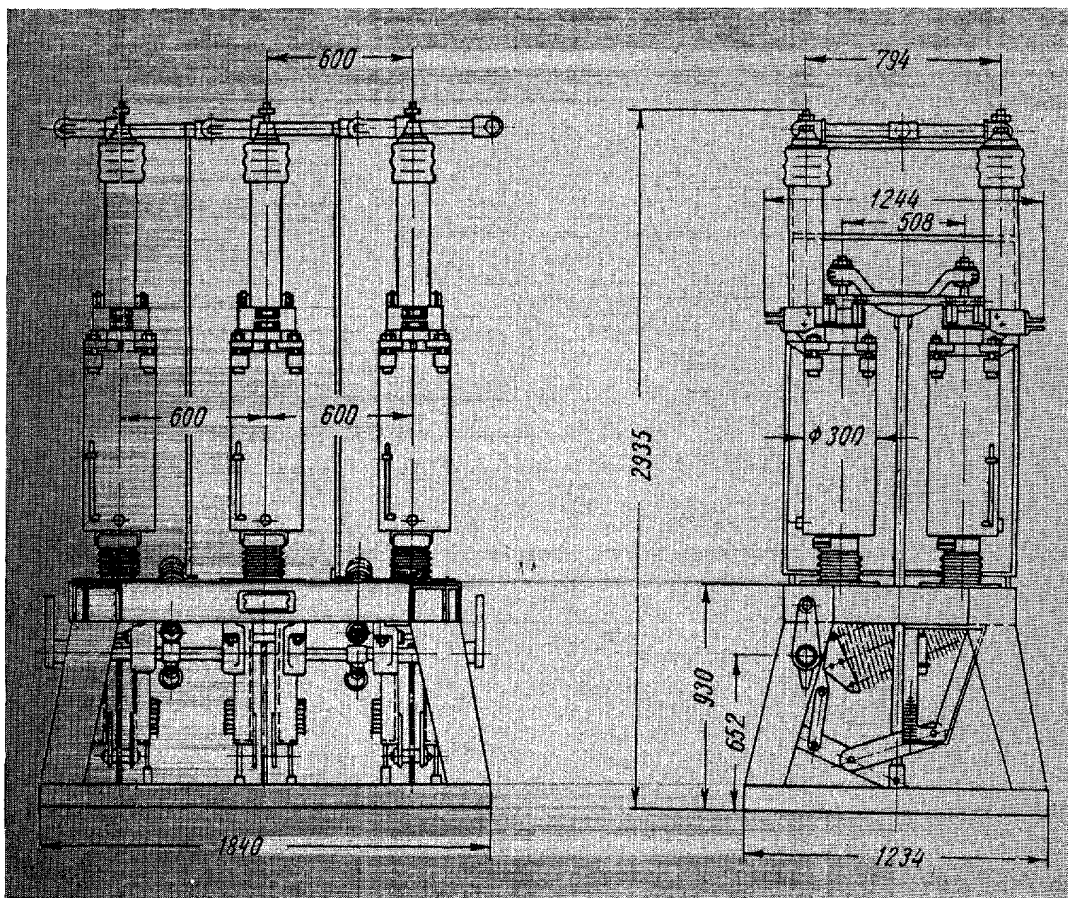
Габаритные размеры выключателя типа МГГ-229М.
